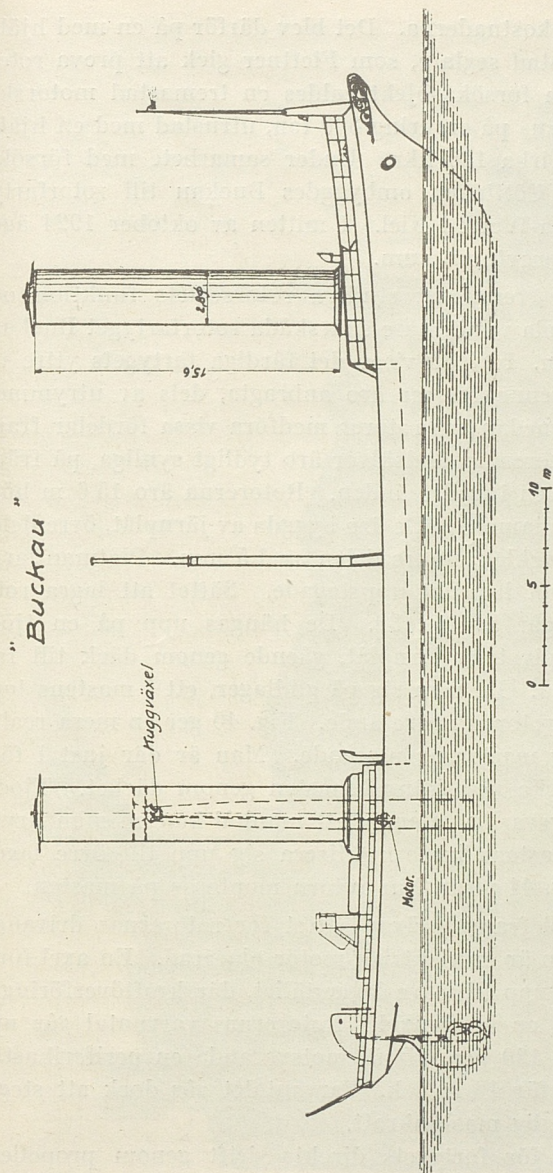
Teckning av Buckau, visande bl. a. dimensionerna av fartyg och rotorer, pivot, elektrisk motor och drivaxel för akterrotorn.
